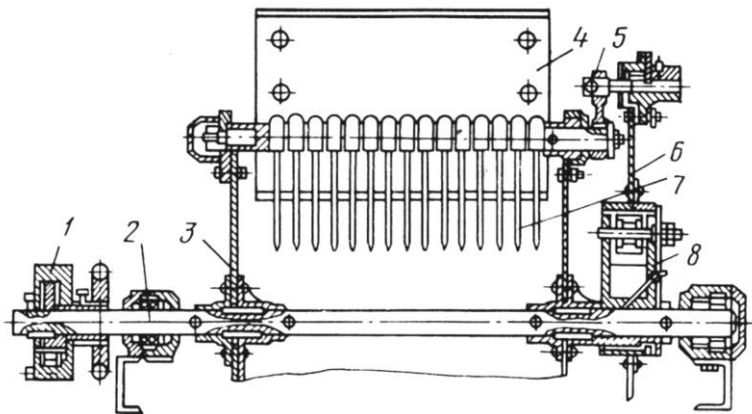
Очесывающий барабан льноуборочного комбайна ЛК-4А:
